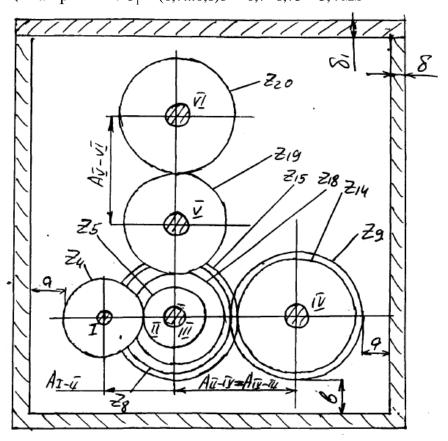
Эскизная компоновка свертки коробки скоростей.
